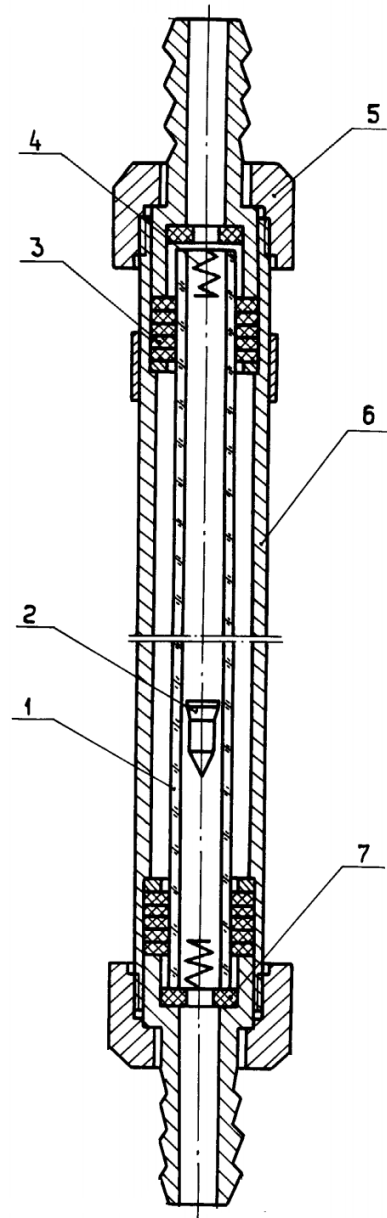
Загальний вид ротаметру типу РМ:
